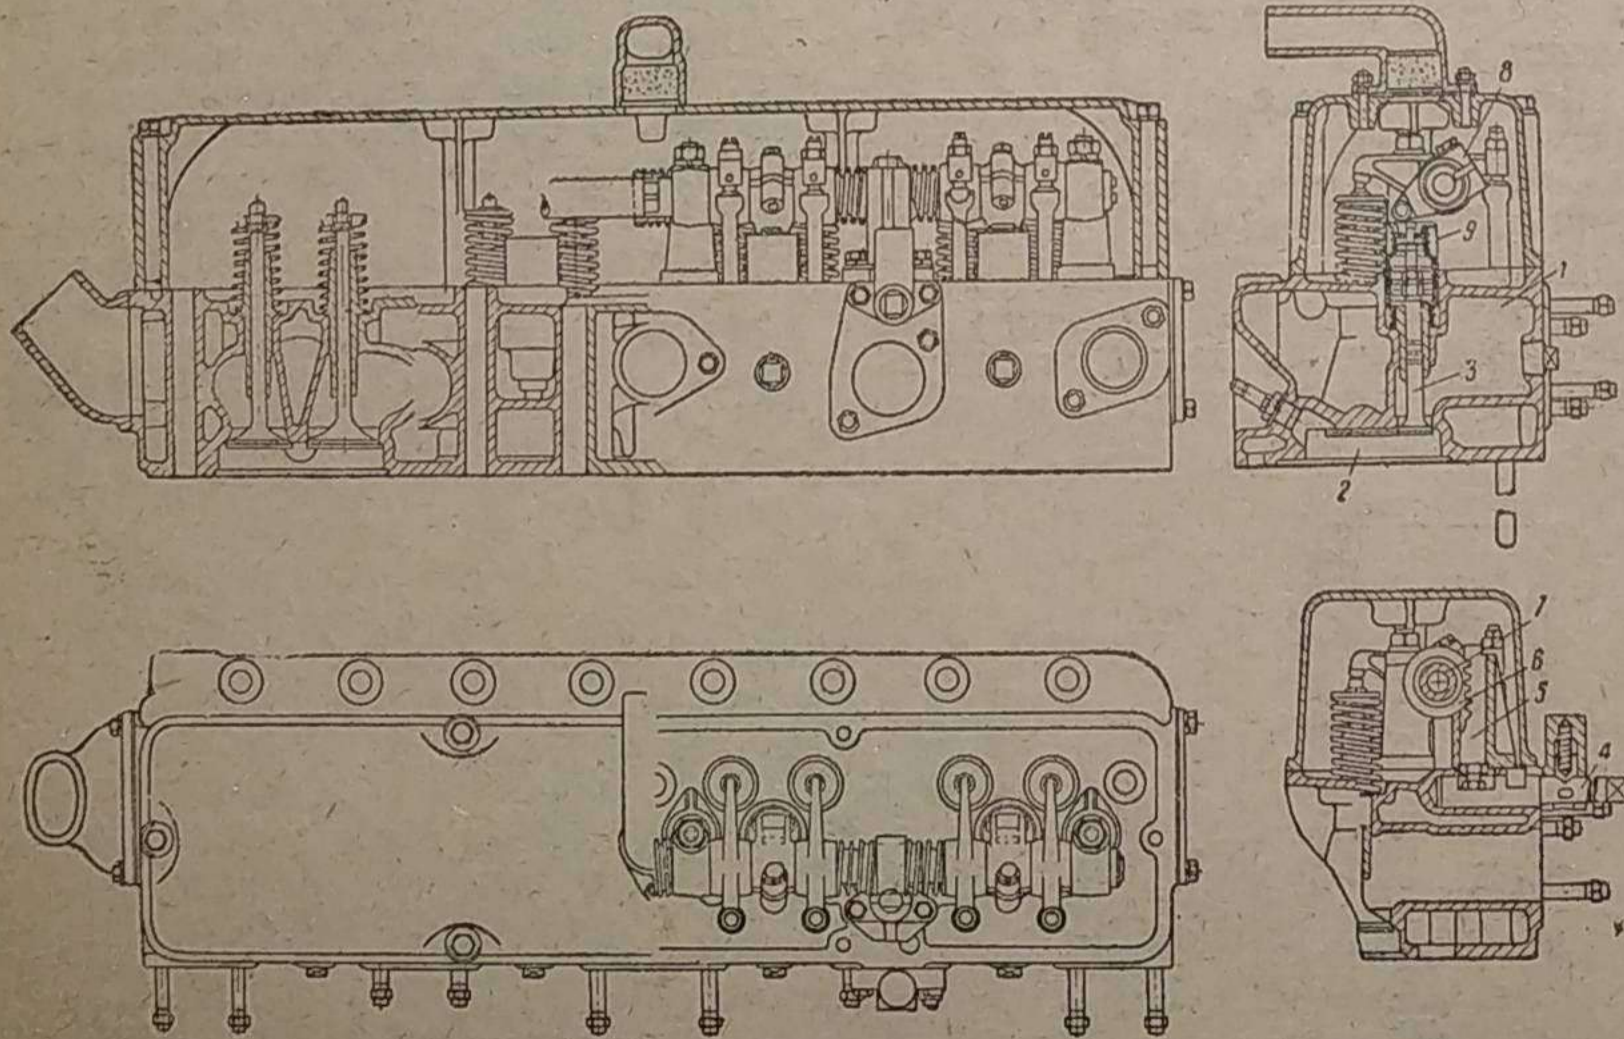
Головка цилиндров двигателя ХТЗ-Т2Г:
